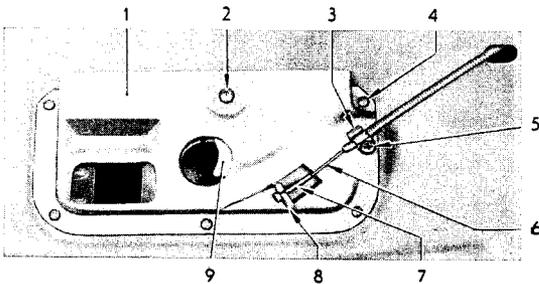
Befestigung des Bowdenzuges für Haubentriegelung am Haubenschluß
